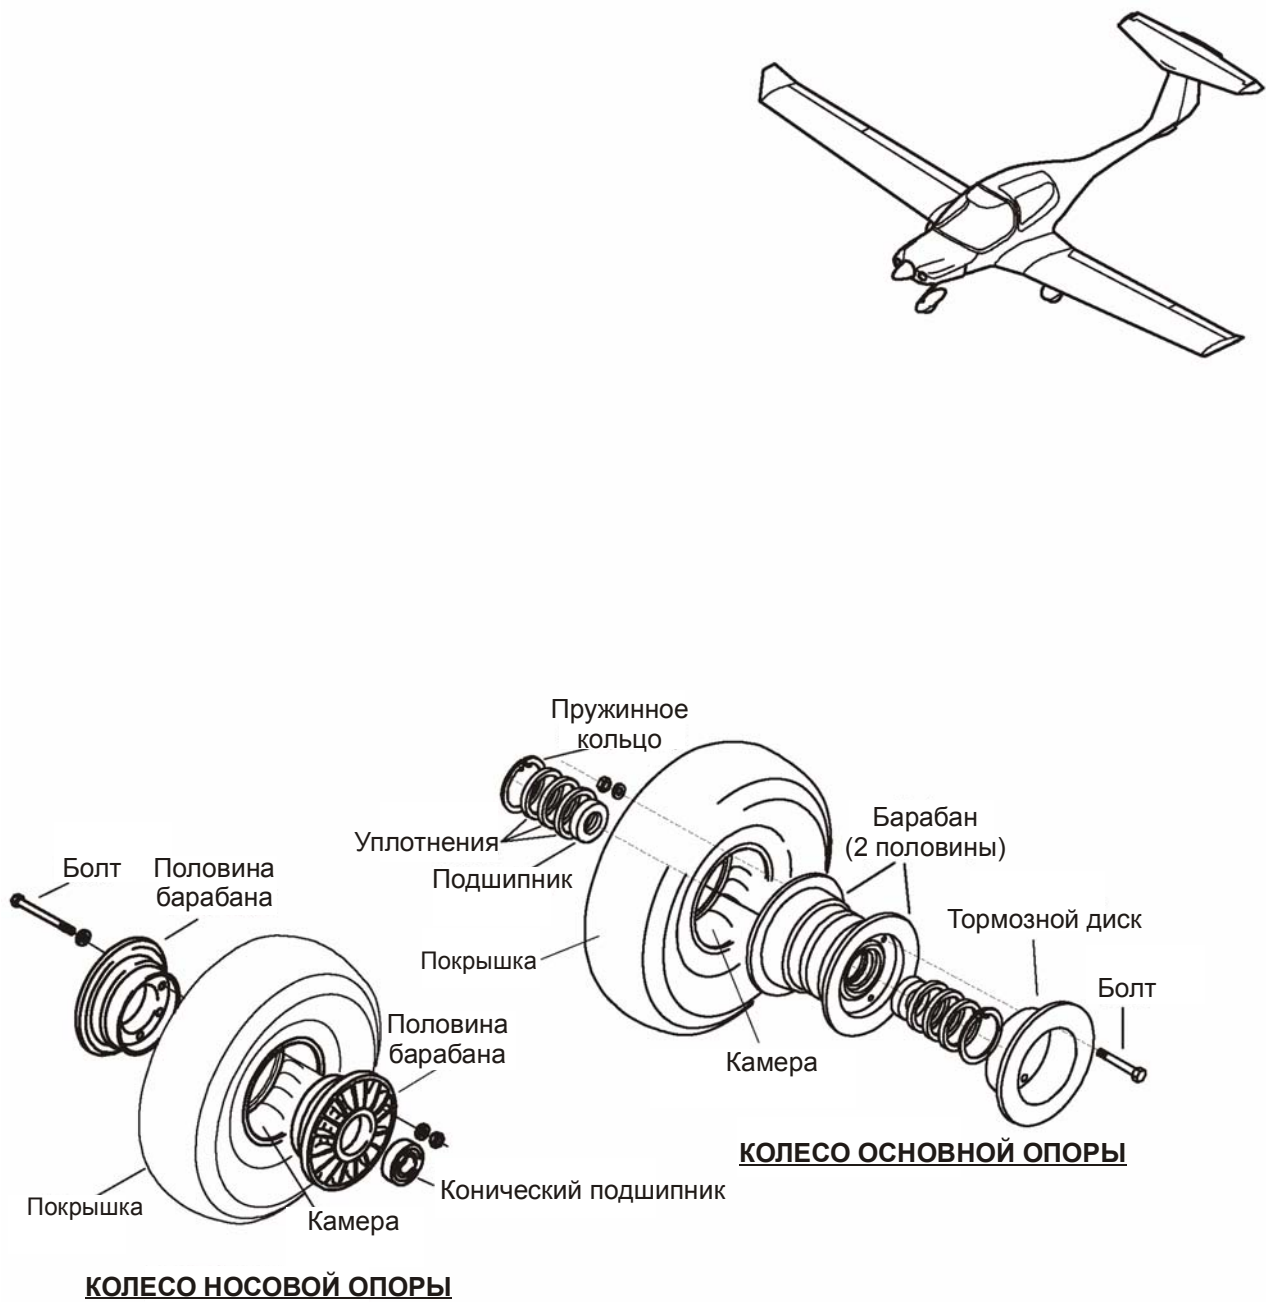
Колесо основной опоры и колесо носовой опоры шасси
